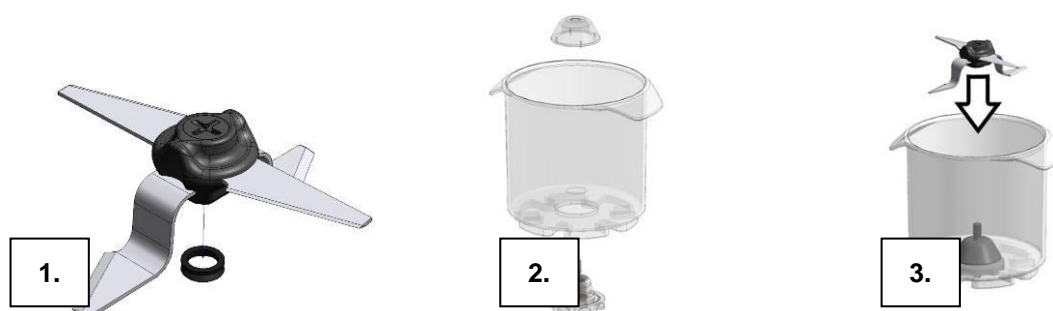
Подготовка ножа и размольного контейнера, установка ножа
